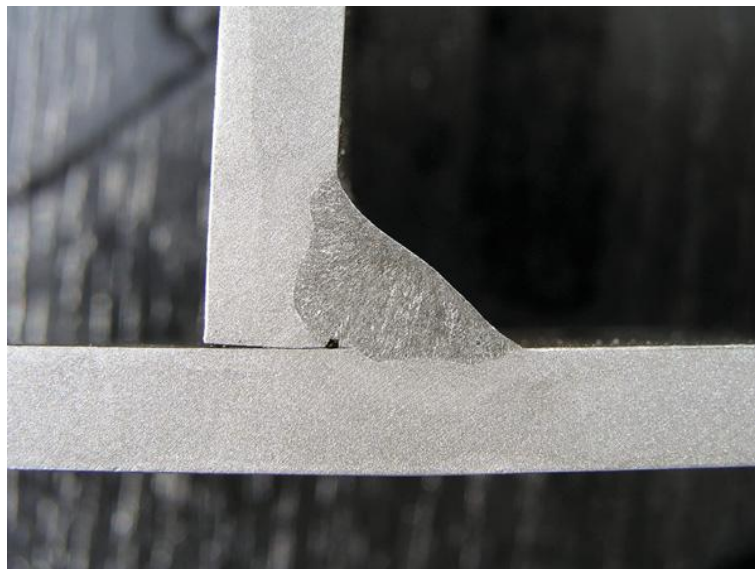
Svarový spoj s neprovařeným kořenem [34].
